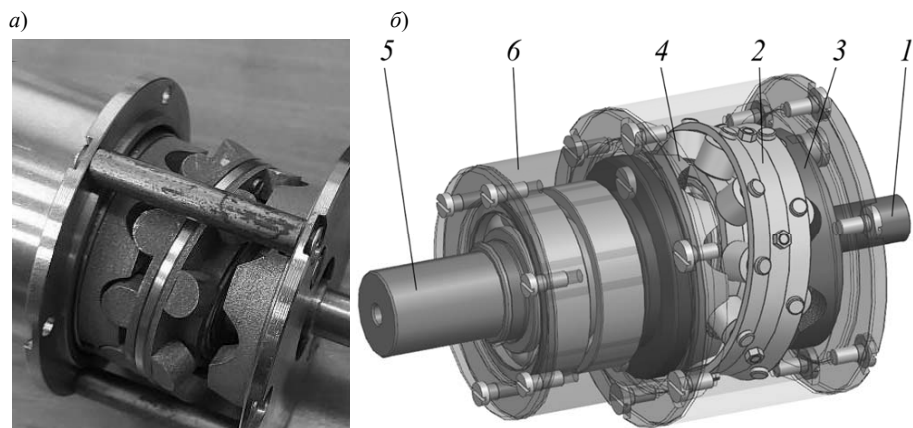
Сферическая роликовая передача: *а* – экспериментальный образец; *б* – модель с вращающимися роликами; 1 – ведущий вал; 2 – сателлит; 3 – неподвижный кулачок; 4 – ведомый кулачок; 5 – ведомый вал; 6 – корпус
